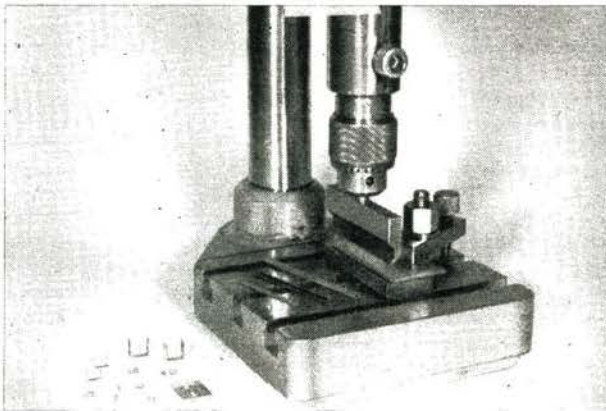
Biegewerkzeug im Einsatz. Als Presse kann eine Tischbohrmaschine dienen, sofern nicht geeignetere Druckerzeuger zur Verfügung stehen.
